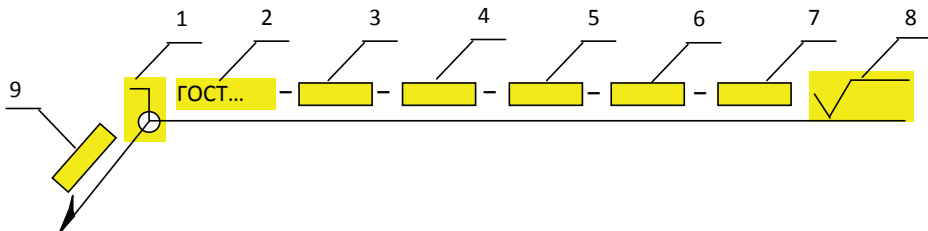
Структура условного обозначения стандартного сварного шва
